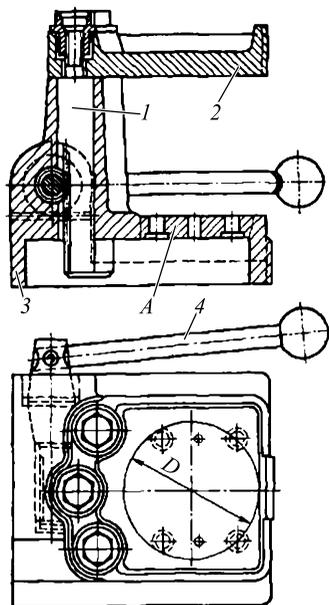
Скальчатые кондуктора с ручным зажимом
